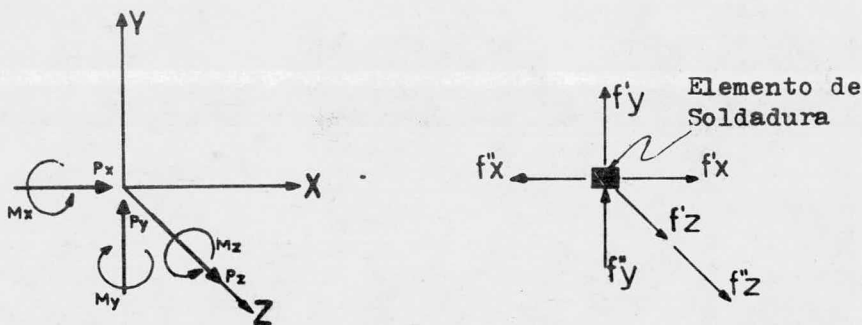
a) Componentes de un Esfuerzo en un Elemento de Soldadura
